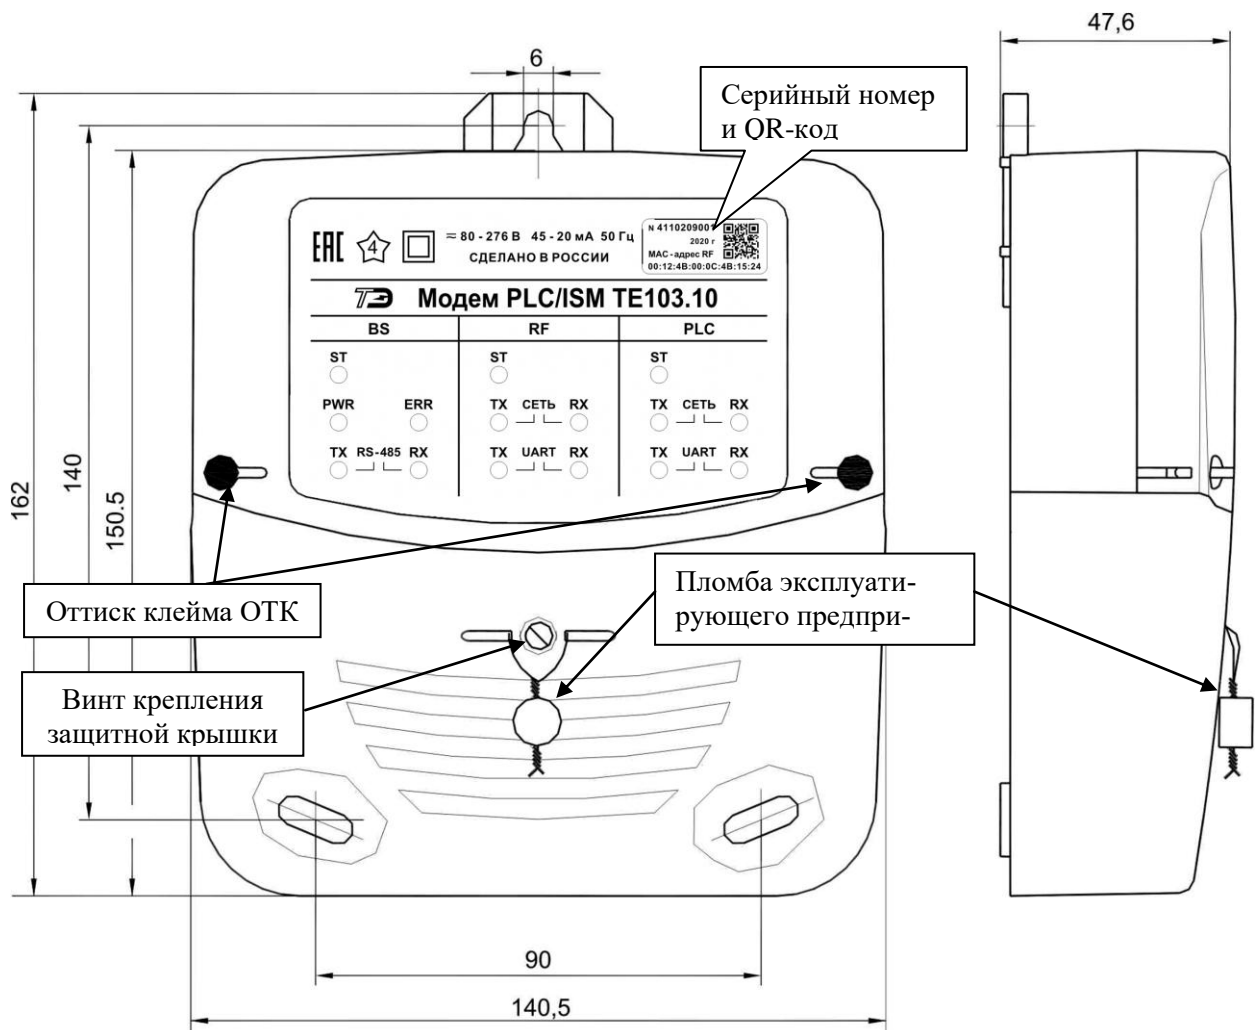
Габаритный чертеж и установочные размеры модемов TE103.10, TE103.01 с защитной крышкой
